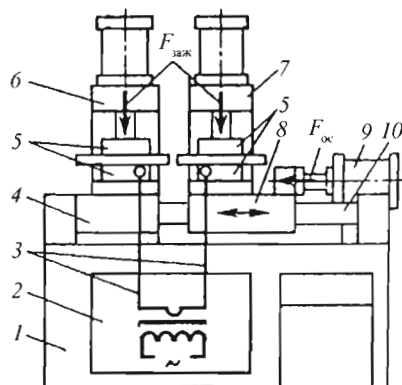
Конструктивная схема машины стыковой сварки:
